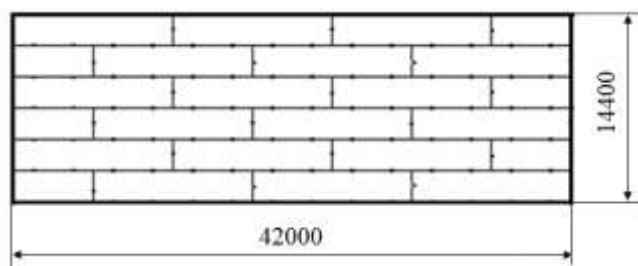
Схема соединения секций палубы и днища в средней части корпуса
